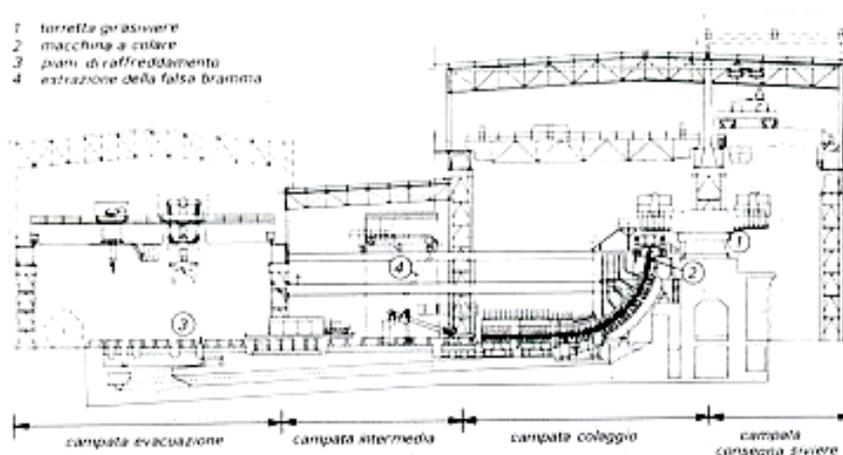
Sezione longitudinale dell'impianto di colata continua
